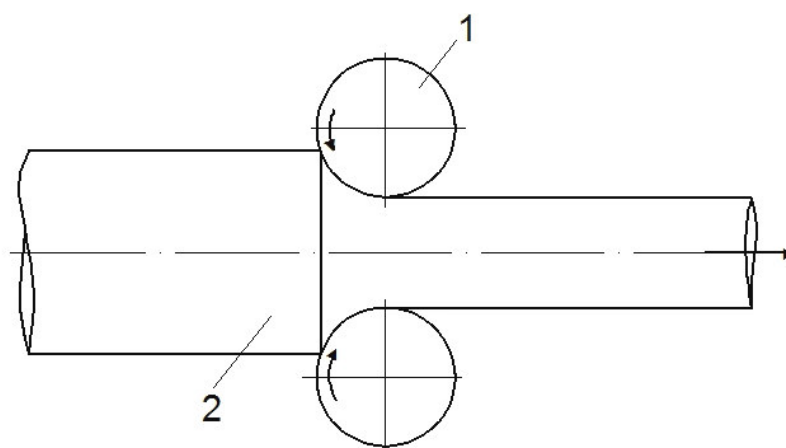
Схема продольной прокатки: 1 – валки, 2 – заготовка
